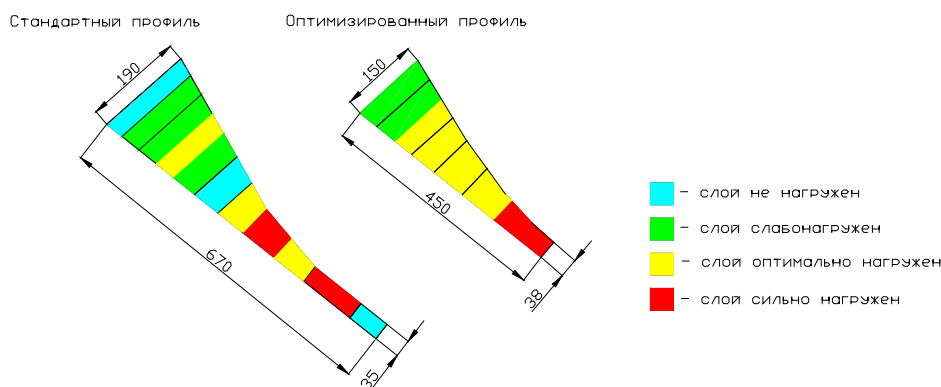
Стандартные и оптимизированные профили камеры дробления конусной дробилки
